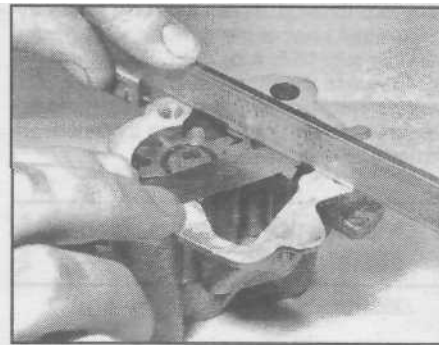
Проверка осевого зазора шестерни масляного насоса
